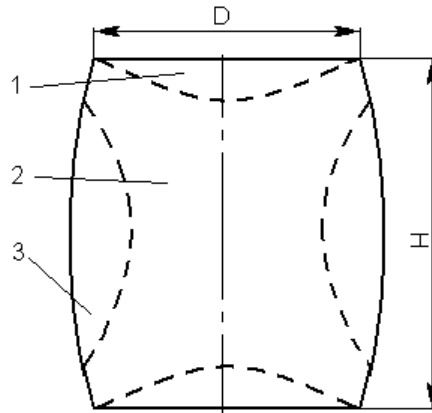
Характерные зоны в заготовке при осадке цилиндра
